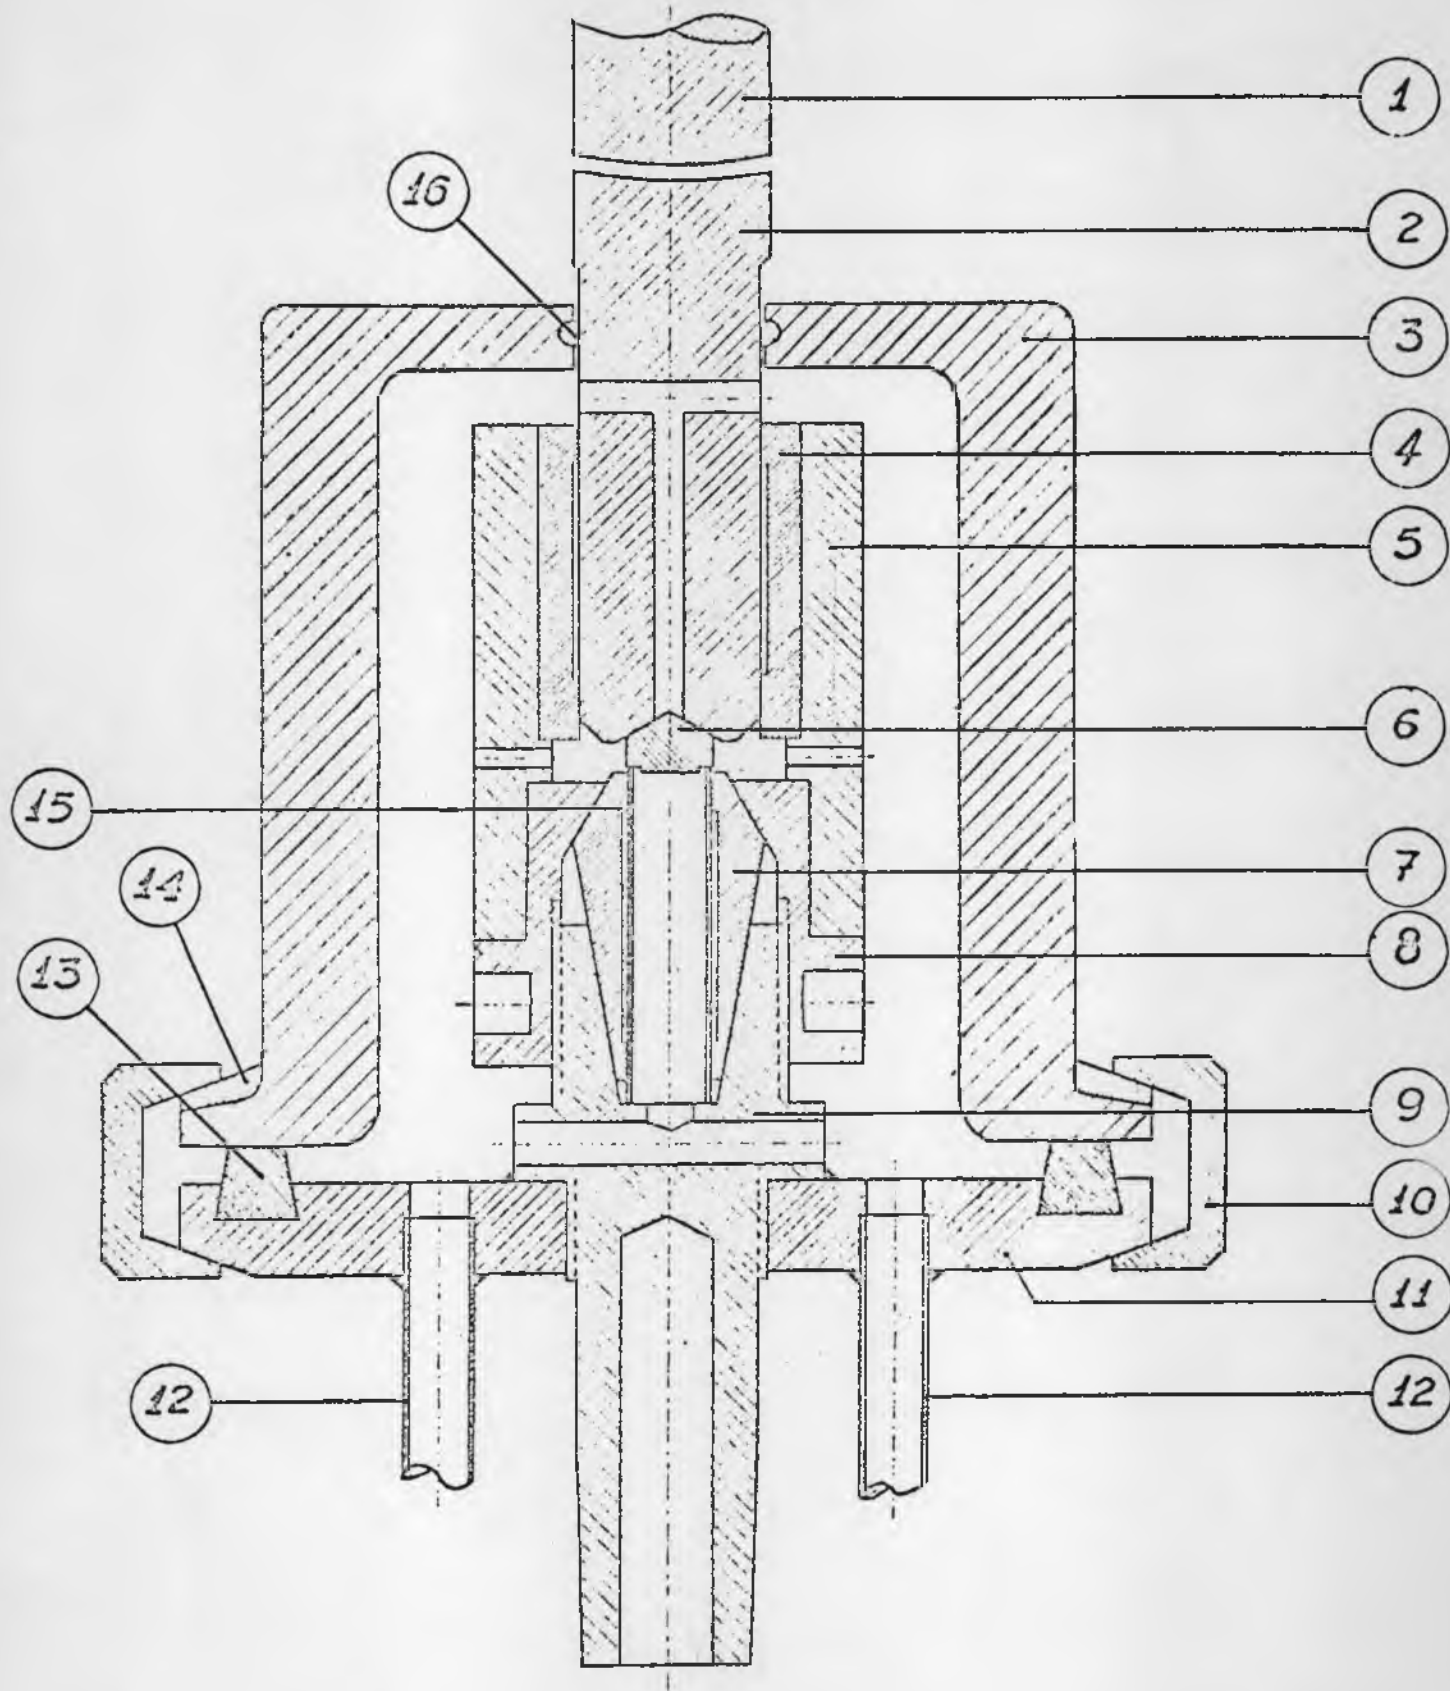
Dispositivo de sujeción de vaina y tapón para soldadura por resistencia.
